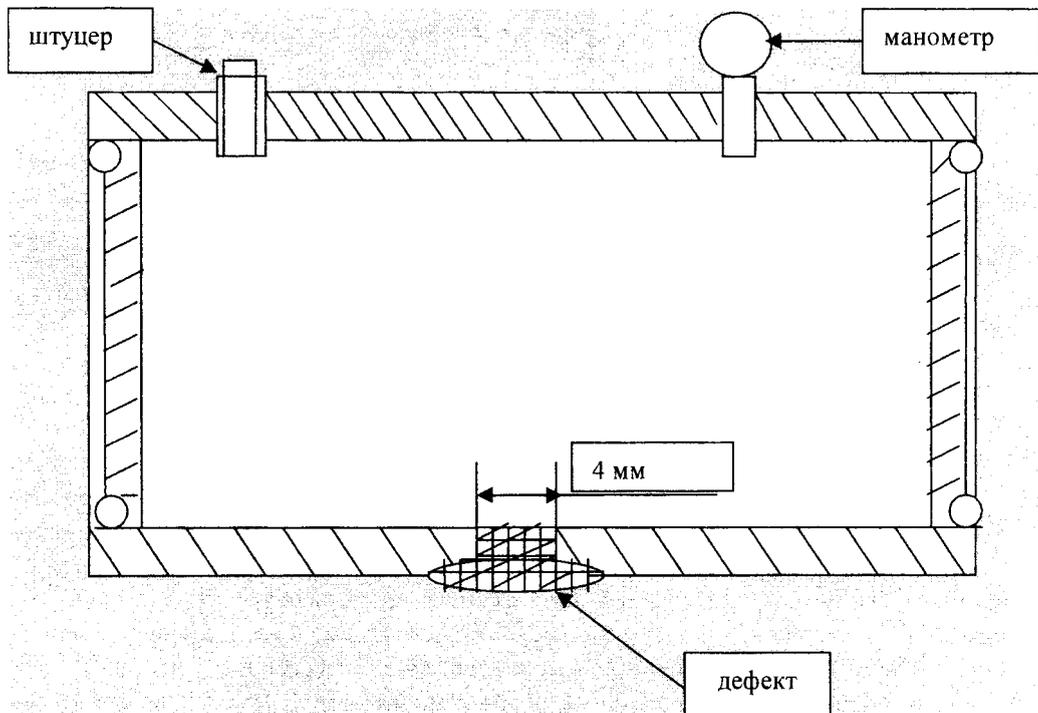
Образец для испытания прочности, плотности и качества ремонта с применением холодной сварки
